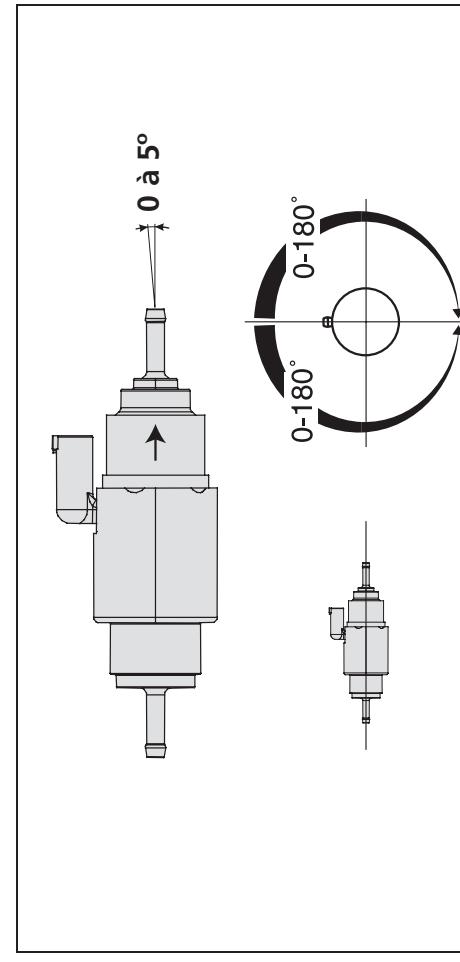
Emplacement de montage de la pompe à carburant DP40
